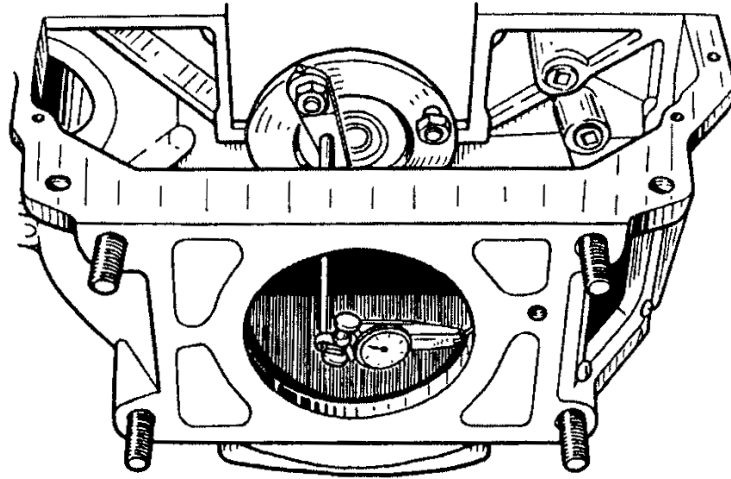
Проверка концентричности установочного отверстия в картере сцепления относительно оси коленчатого вала
